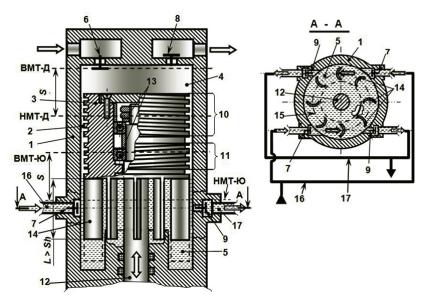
Схема крейцкопфного варианта ГЭМОД с вращающимся лабиринтным уплотнением: 1 — цилиндр; 2 — зазор; 3 — поршень; 4 — компрессорная полость; 5 — насосная полость; 6 и 7 — всасывающие клапаны; нагнетательные клапаны; 10 и 11 — винтовые разнонаправленные поверхности; 12 — шток; 13 — подшипниковый узел; 14 — лопатки; 15 — окружность, плоскость которой перпендикулярна оси цилиндра; 16 — линия всасывания жидкости; 17 — линия нагнетания жидкости; ВМТ-Д и НМТ-Д — верхняя и нижняя мертвые точки днища поршня; ВМТ-Ю и НМТ-Ю — верхняя и нижняя мертвые точки положения юбки поршня
